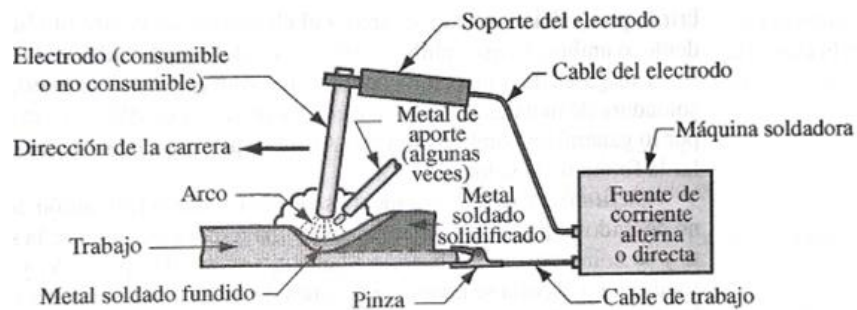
Configuración básica y circuito eléctrico de un proceso de soldadura con arco. Fuente: Groover, M. (2007). *Fundamentos de manufactura moderna* (3rd ed.)
